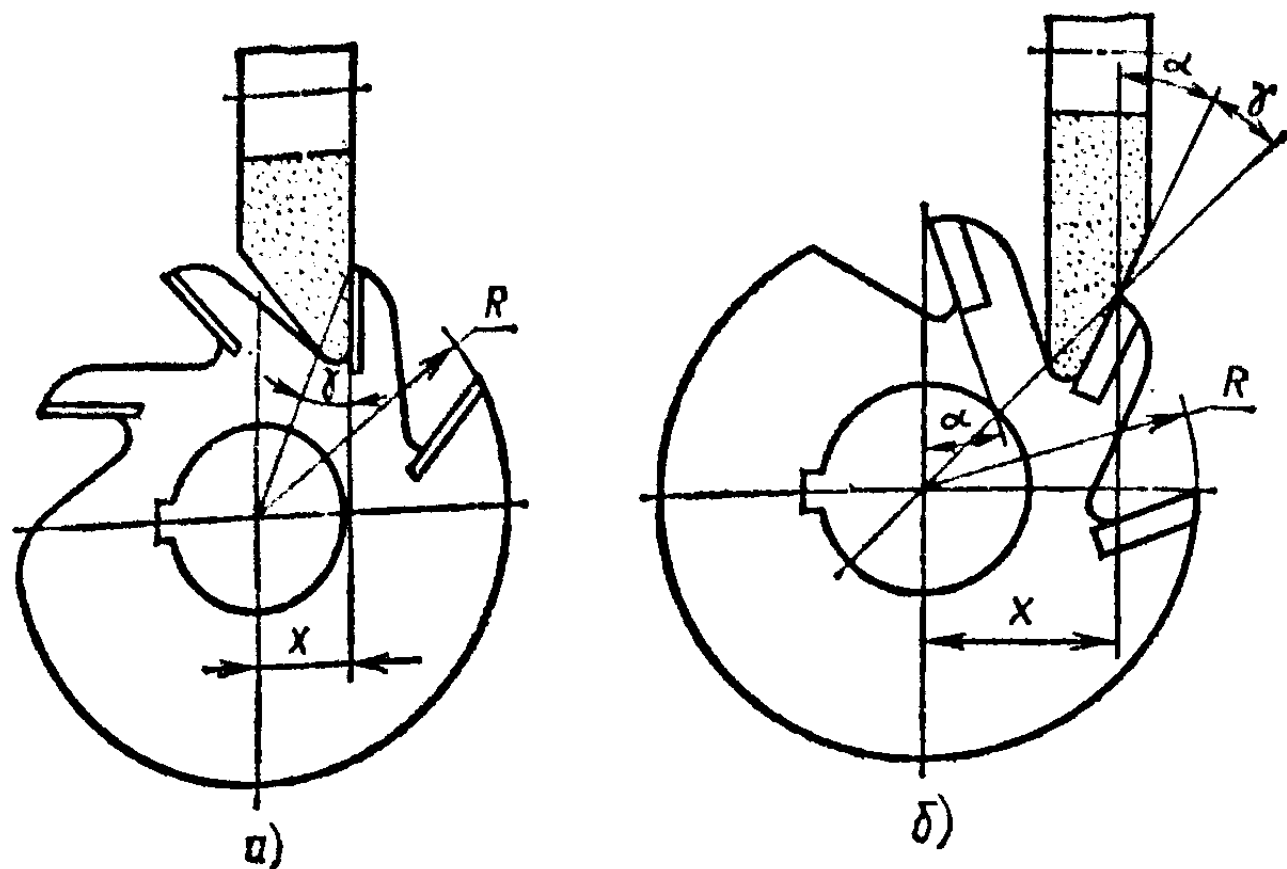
Схема заточки фрез по передней поверхности лезвия:
